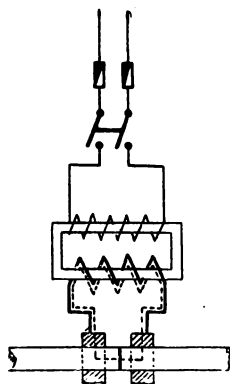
Soldadura eléctrica por resistencia empleando corriente alterna.
